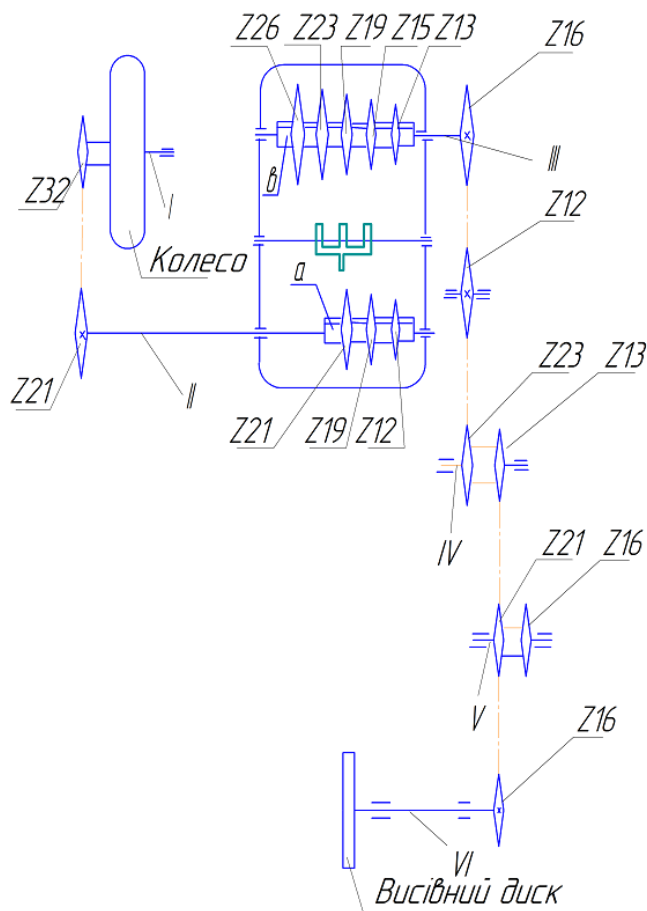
Кінематична схема механізму привода сівалки СУПН-8
